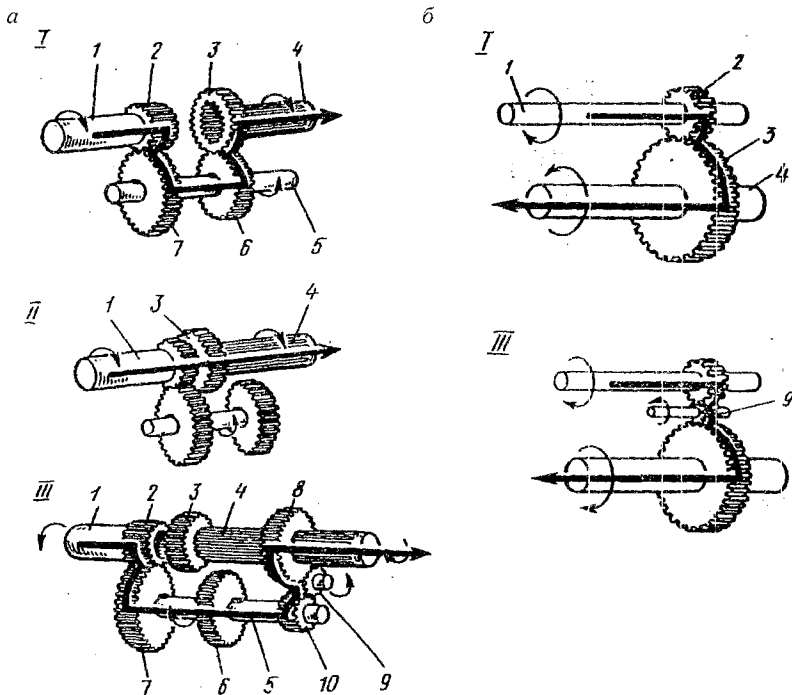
Схема работы трехвальной (а) и двухвальной (б) коробок передач при включении понижающей (I), прямой (II) передач и передачи заднего хода (III): 1, 5 – первичный и промежуточные валы; 2 – шестерня первичного вала; 3, 8 – шестерни вторичного вала; 4 – вторичный вал; 6, 7, 10 – шестерни промежуточного вала; 9 – промежуточная шестерня
